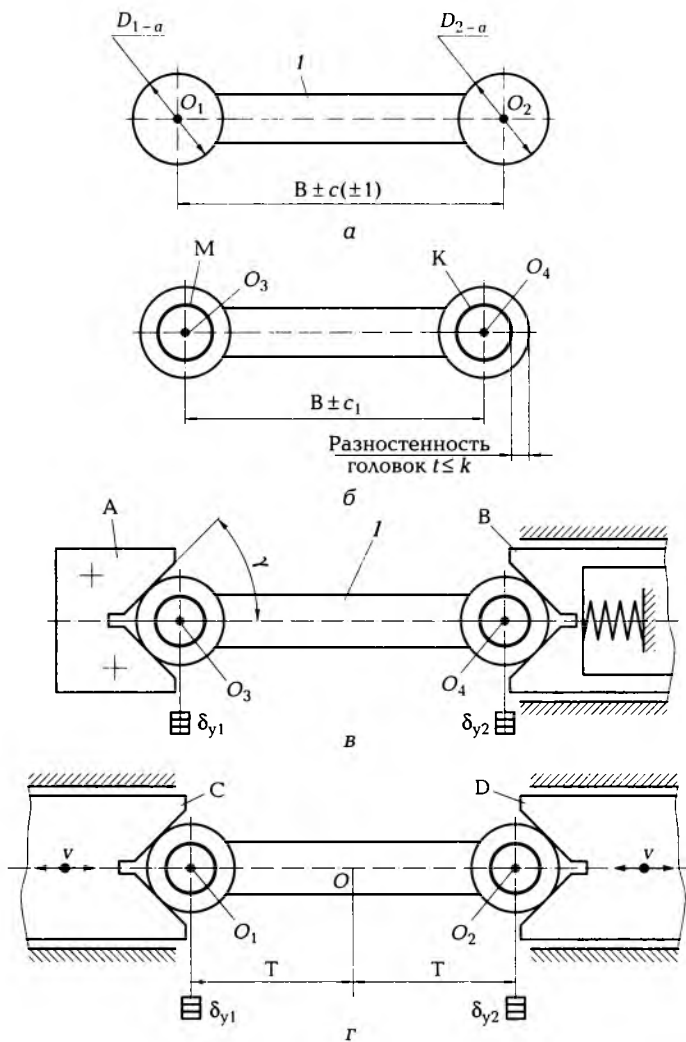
Пример установки заготовки для обработки двух отверстий:
